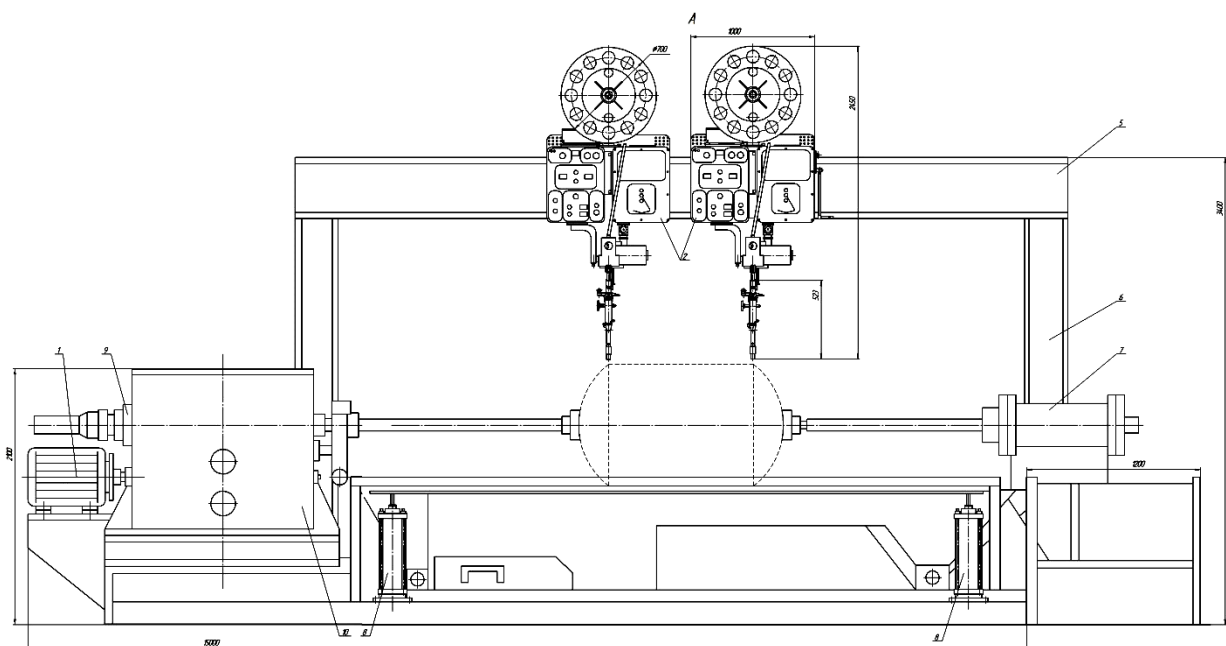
(Вигляд з боку) установки для складання і автоматичного зварювання обичайки ресивера із півсферичними днищами
